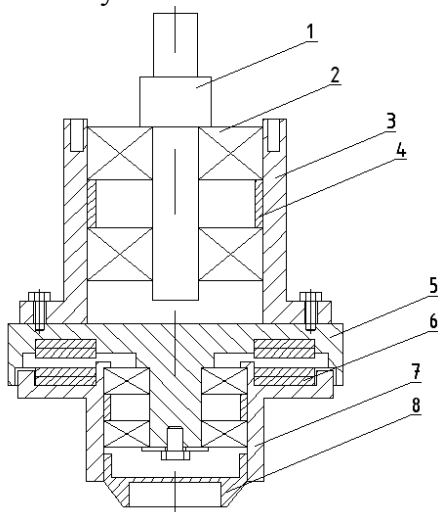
Закупорювальний патрон для ПЕТ-пляшок:
